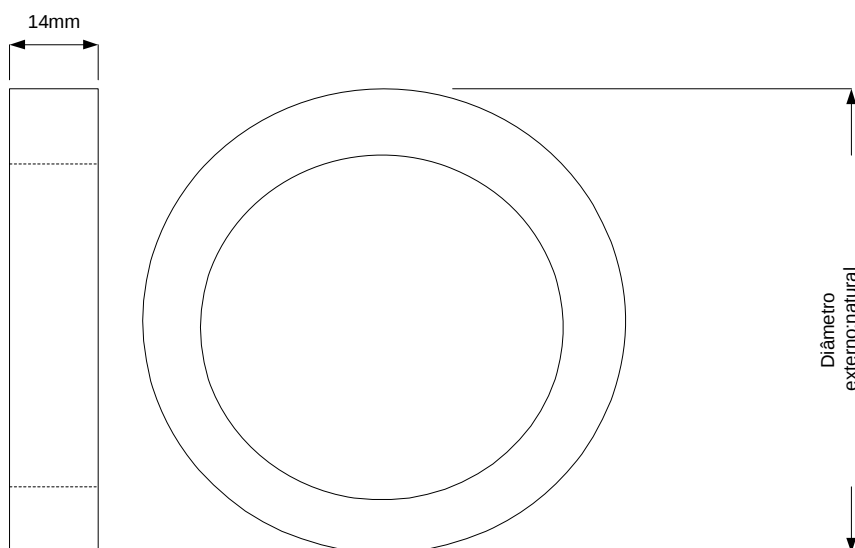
Representação do corpo de prova utilizado no torno mecânico e dispositivo laminador.
